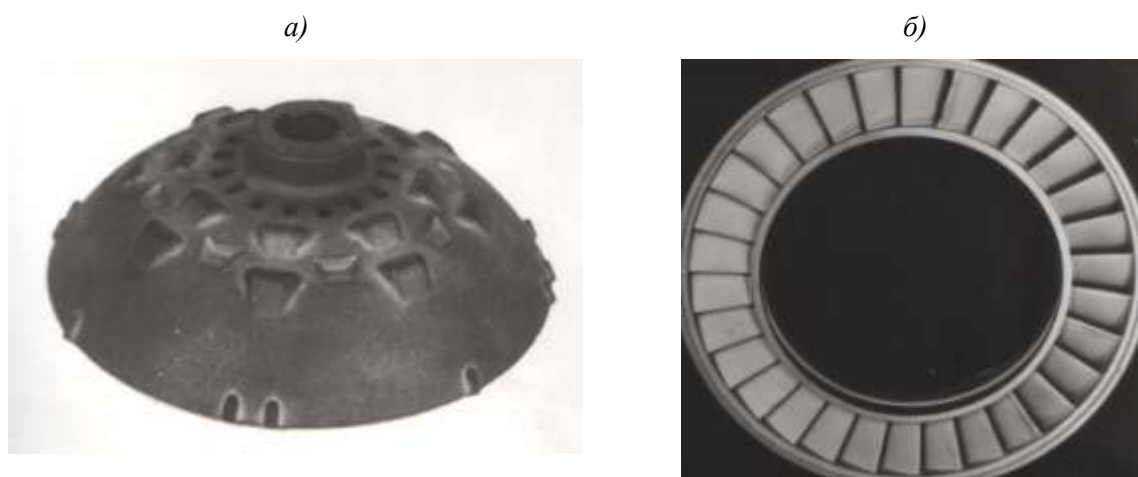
Отливки из интерметаллидного сплава ВКНА-4
